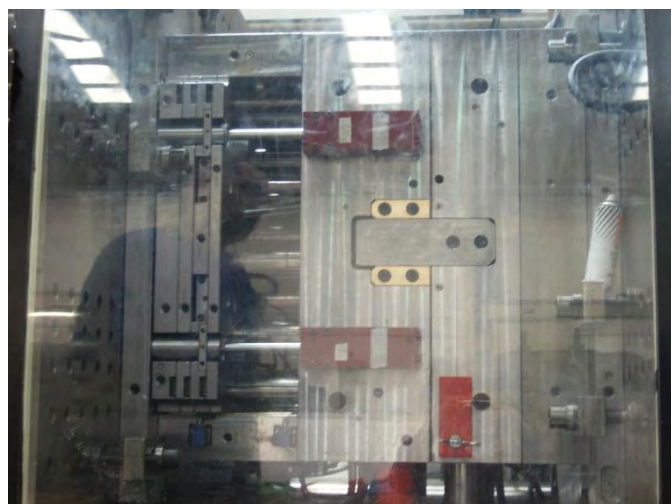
Vista real do molde 7191 em ciclo de injeccção.
